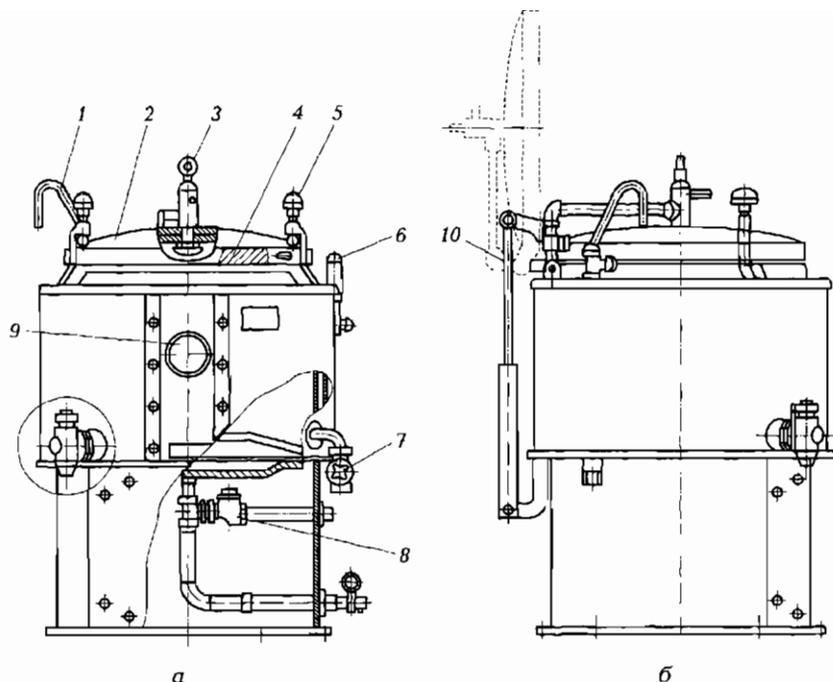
Котел пищеварочный паровой КПП-250:
